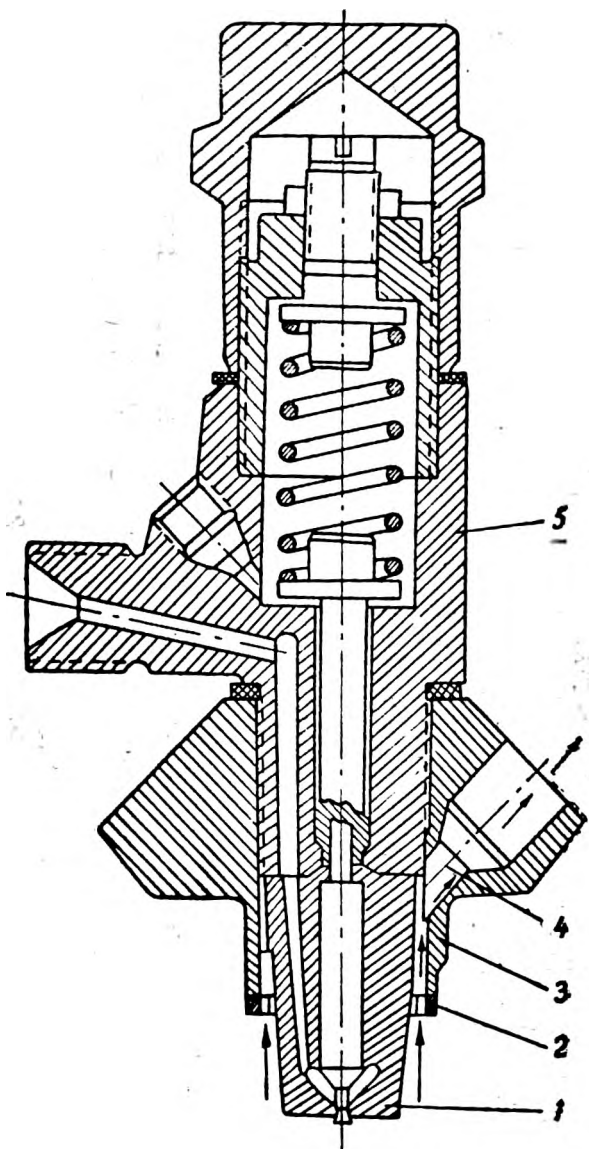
Форсунка с головкой-датчиком для отбора давления газов из цилиндра двигателя.
